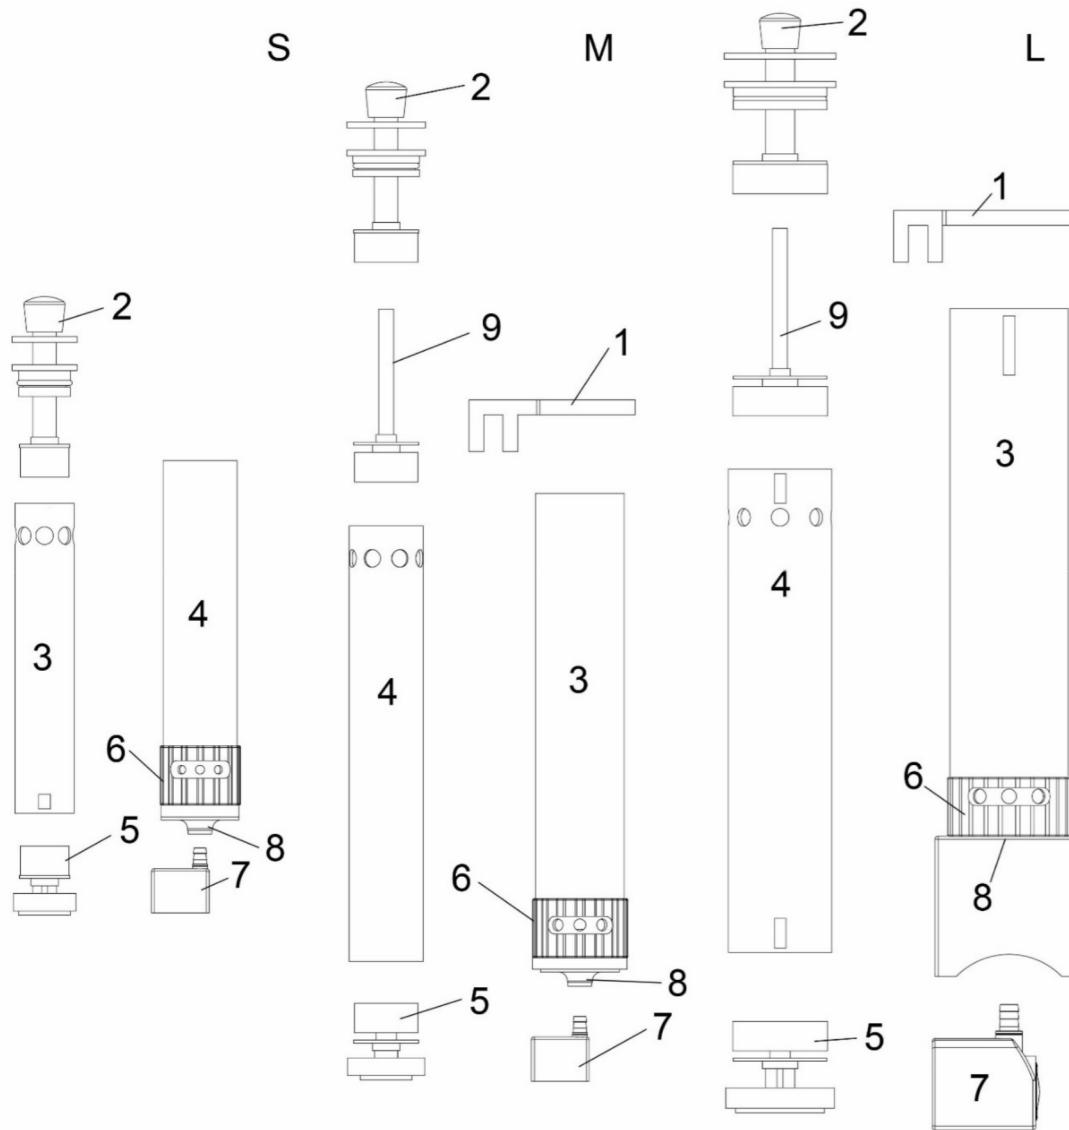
1. Mocowanie 2. Pokrętło (regulator przepływu) 3. Gąbka 4. O-ring (S + M: 2 O-rings, L: 1 O-ring)
